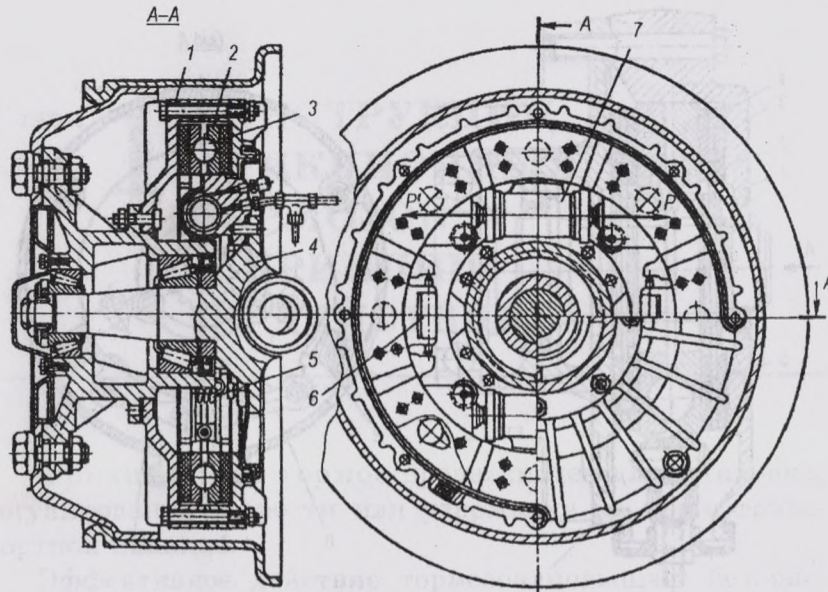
Дисковый тормоз НАМИ-ЛАЗ: 1 – корпус; 2 – нажимной диск; 3 – шарик; 4 – невращающаяся полуось колеса; 5 – пружина; 6 – автоматический компенсатор износа фрикционных накладок; 7 – гидроцилиндр
